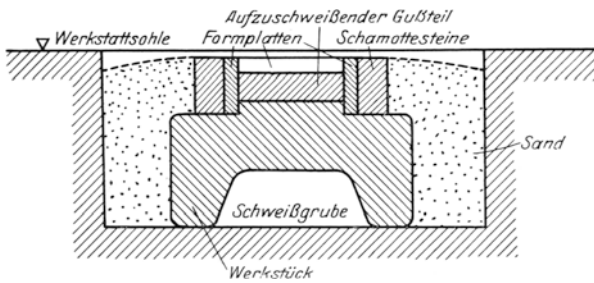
Einförmung eines Warmschweißstücks ohne Formkasten.
